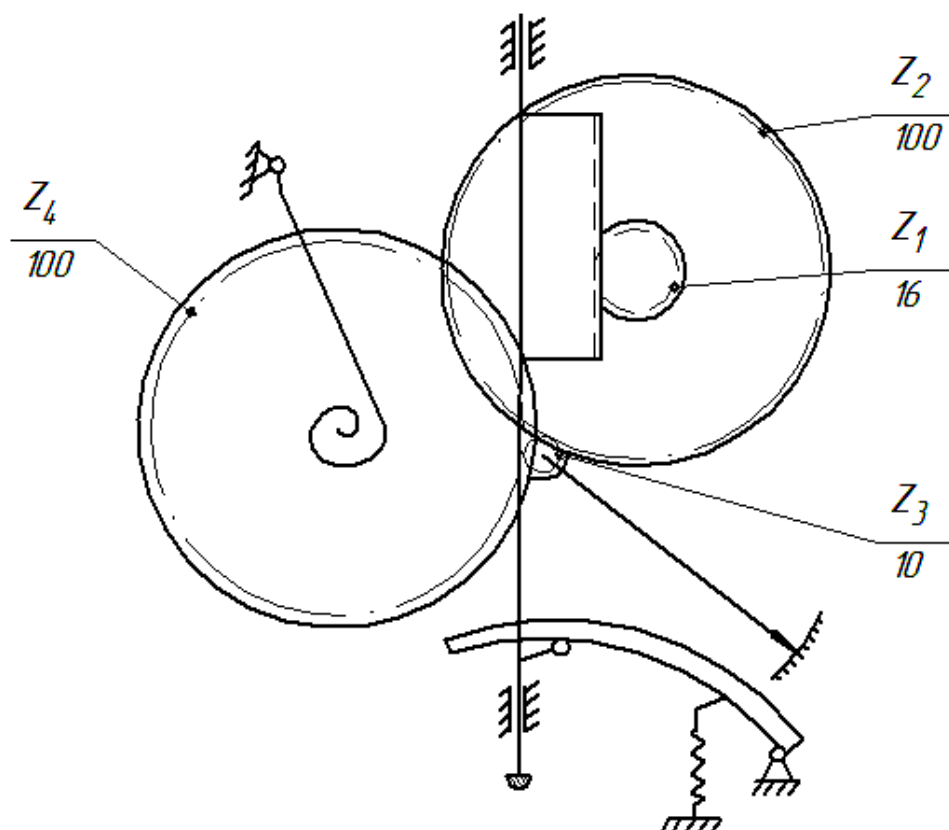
Кинематическая схема индикатора часового типа
